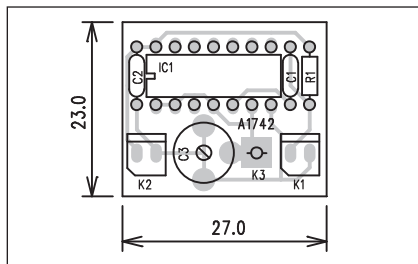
Obrazec desky spojů spínače (strana BOTTOM)
